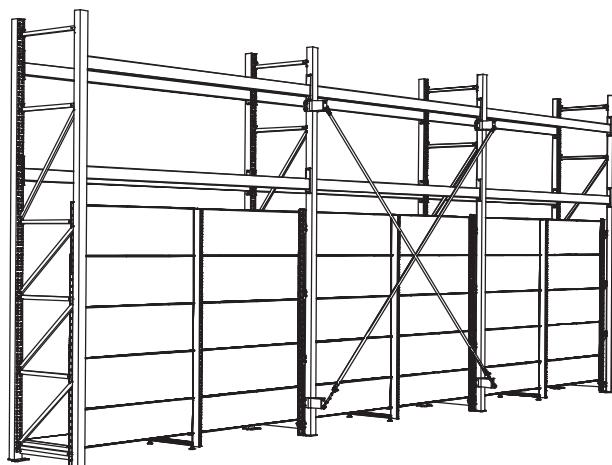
Задняя стенка стеллажа с перекрестными связями
